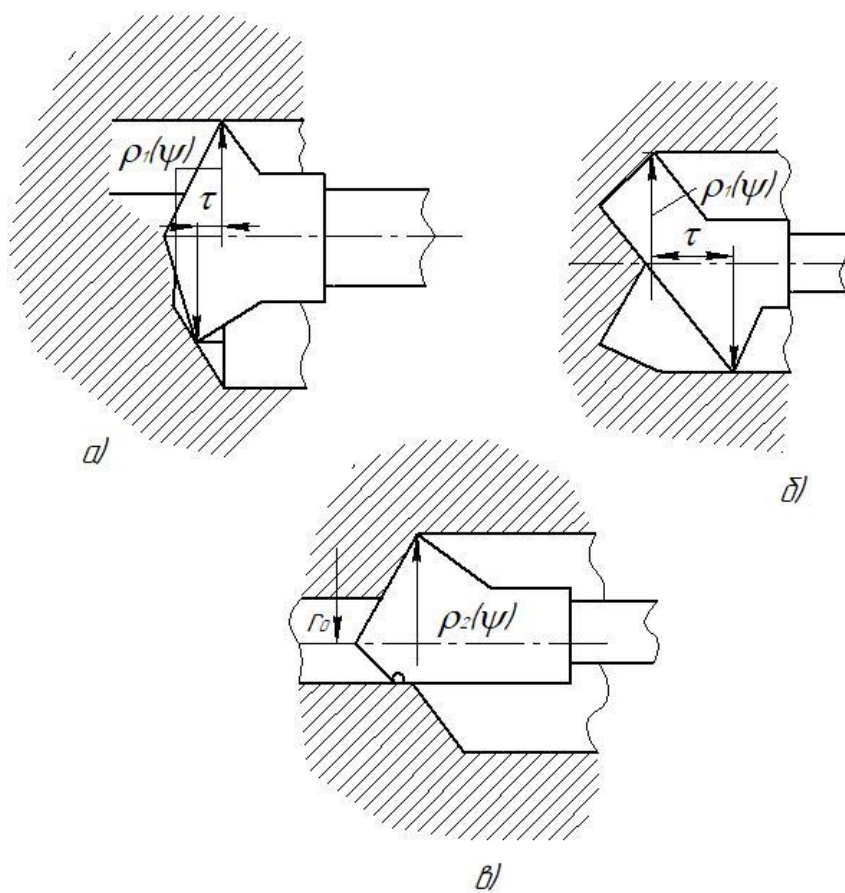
Схемы обработки с базированием инструмента: а) на поверхность резания, б) на обработанную поверхность, в) на предварительно обработанную поверхность.
